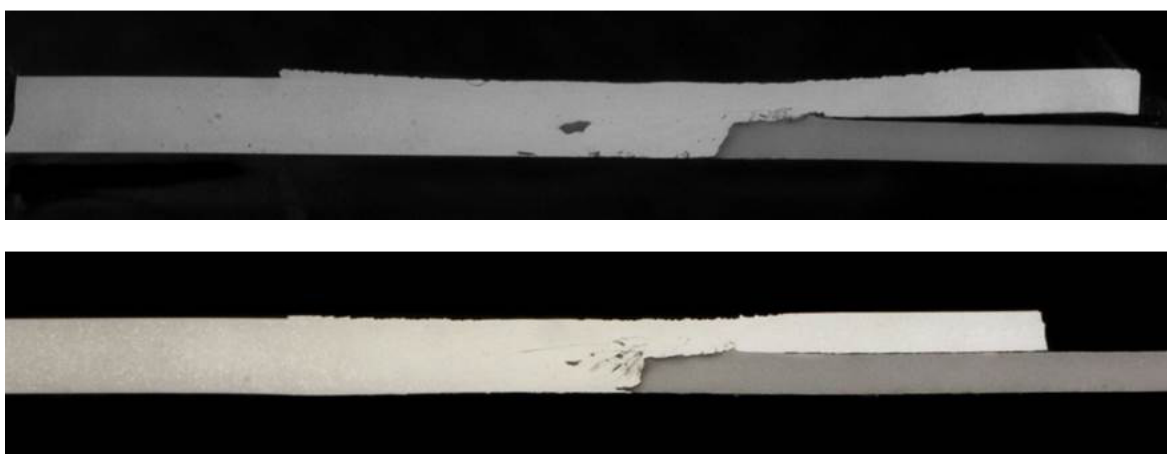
Schliffbild der Naht geschweißt mit breitem (oben) und schmalen (unten) Werkzeug
